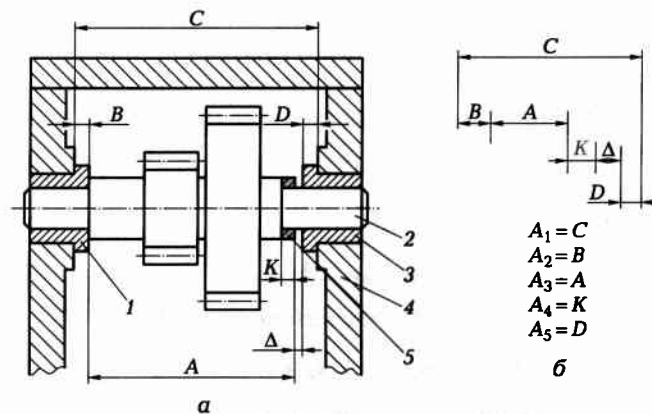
Сборочный чертеж редуктора со сменным компенсатором: а — сборочный чертеж; б — схема сборочной размерной цепи
